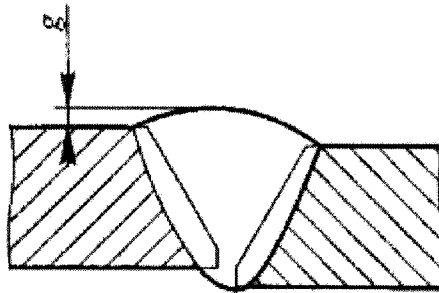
Измерение выпуклости стыкового шва (g) при различном уровне наружных поверхностей деталей, вызванном смещением при сборке соединения под сварку
